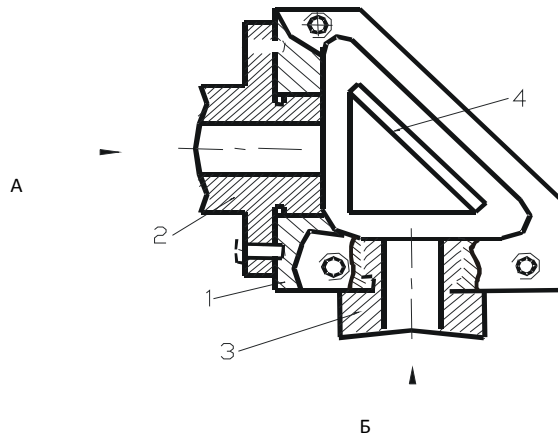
Призмовий вузол: 1 – корпус; 2 – фланцевий тидис; 3 – різьбовий тидис; 4 – призма AP - 90°
